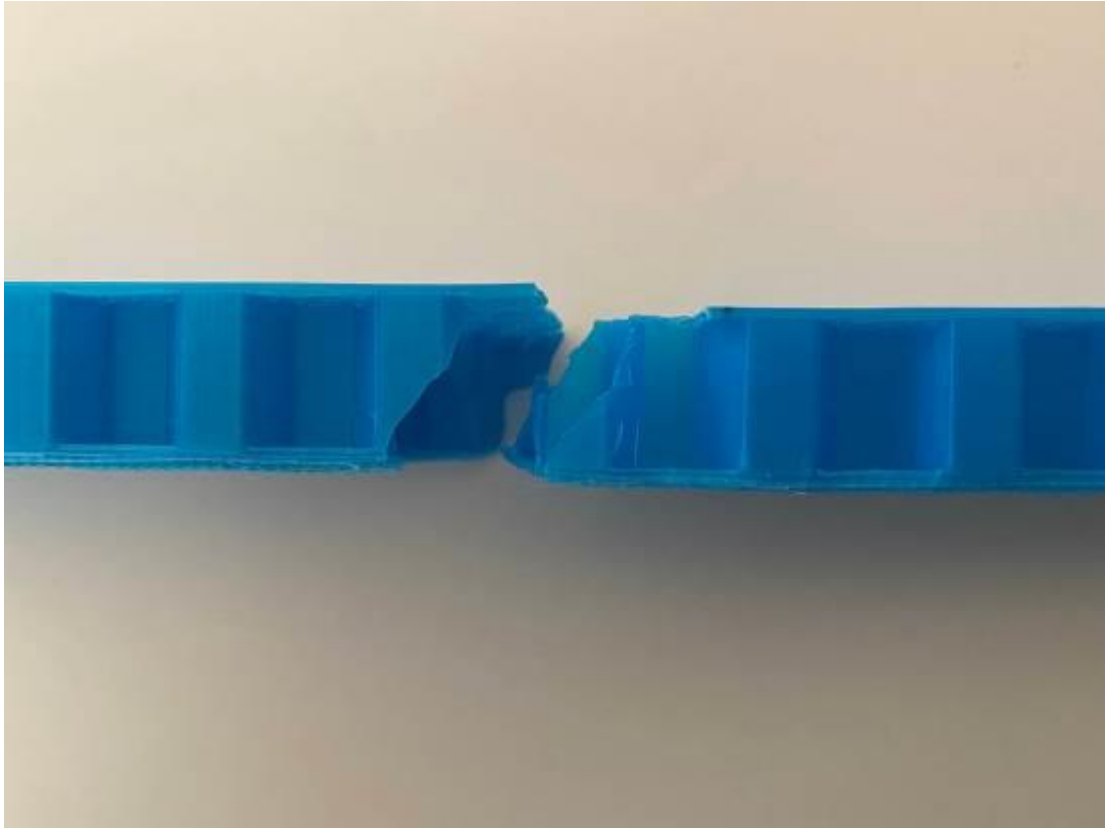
Espécimen 3 del lote de 3/8" fabricado completamente en PLA con tratamiento térmico, tipo de falla X-A-F.
